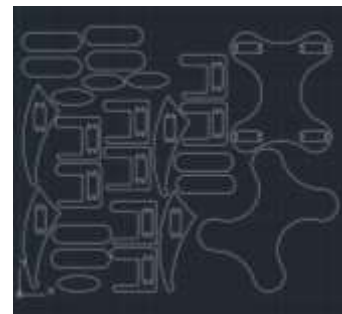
Diseño Cuadrúpedo Explorador en AutoCAD
